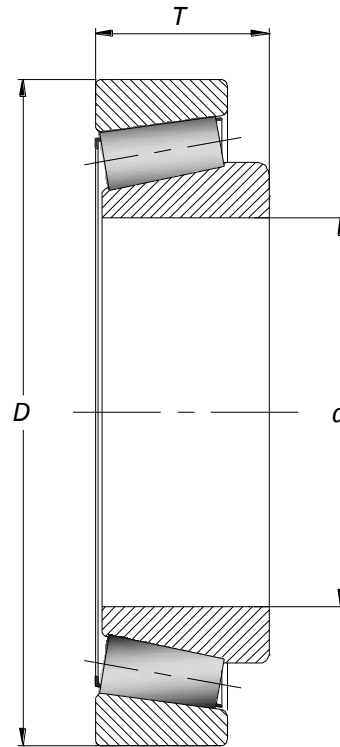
Dimensiones generales del rodamiento HM 51844/10.
